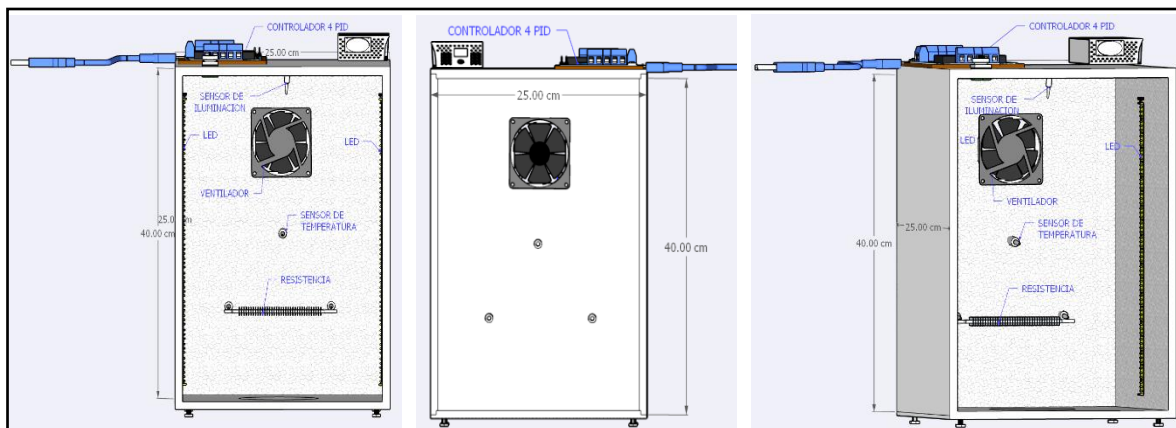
Diseño final, vista frontal, posterior e isométrica.
